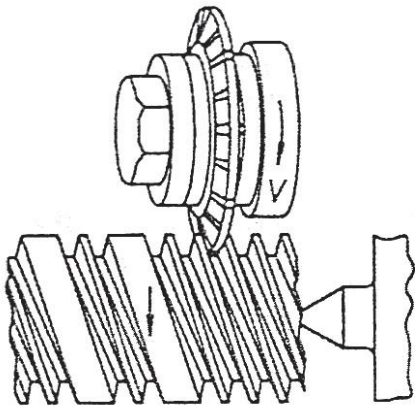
Схема нарезания червяка дисковой фрезой на резьбофрезерном станке
